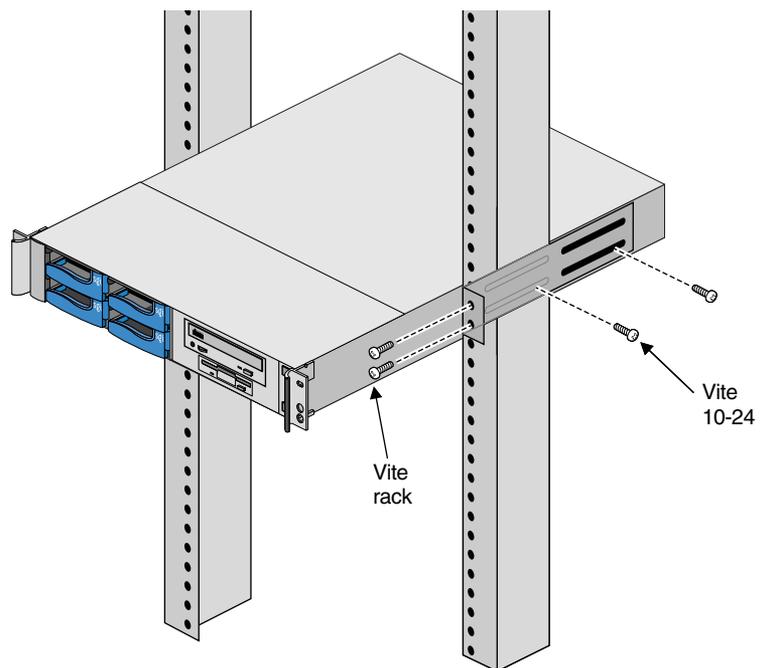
Installazione del telaio in un rack a montaggio centrale
